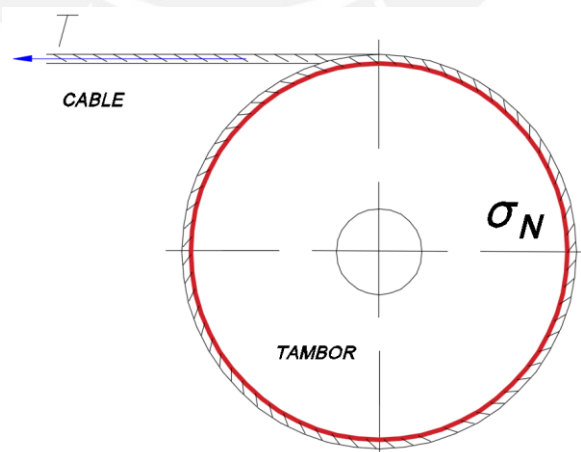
Zona de aplastamiento en el cable tractor enrollado
